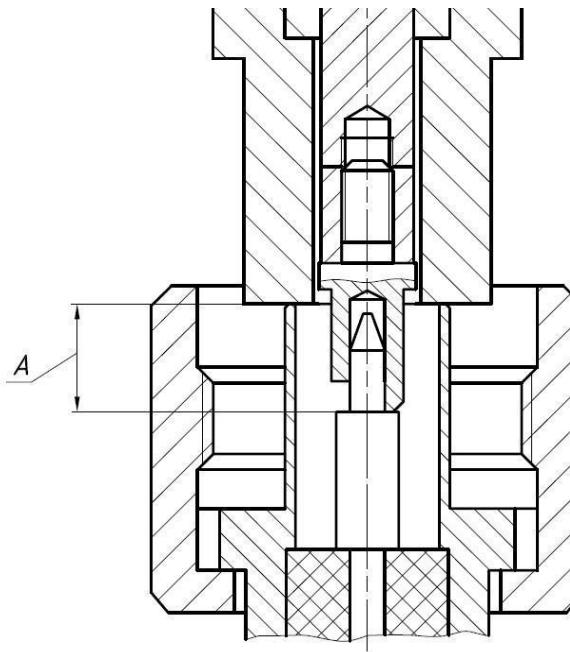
Проверка размера «А» соединителя «вилка»
